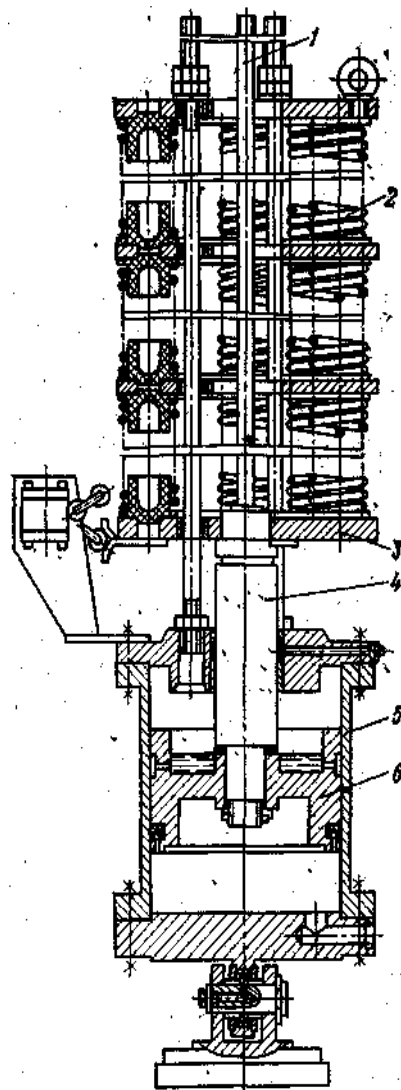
Пружинний пневматичний безвантажний привід гальма
